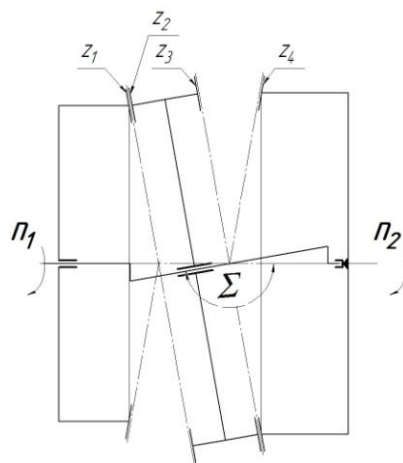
Кинематическая схема редуктора с плоско-конической прецессирующей передачей
